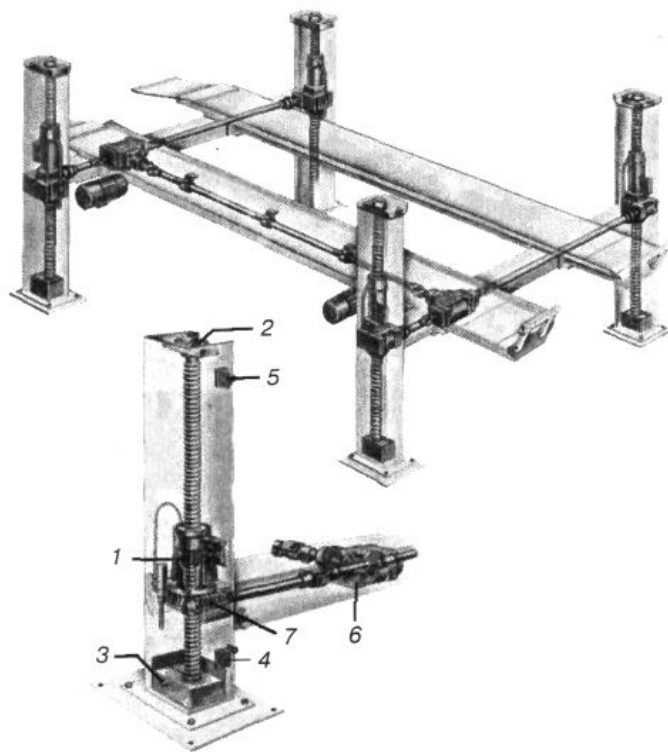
Конструктивная кинематическая схема электромеханического четырехстоечного подъемника КР 440 RAVAGLIOLI (Италия): 1 — блок рабочей и страховочной гаек; 2, 3 — верхняя и нижняя опоры; 4, 5 — верхний и нижний конечные выключатели; 6 — конический редуктор; 7 — червячный механизм
